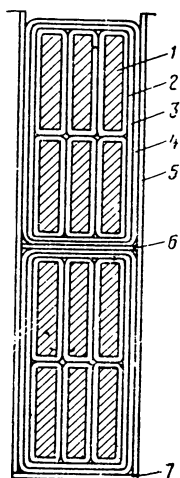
Расположение обмотки в пазу, якоря двухмашинного агрегата:
